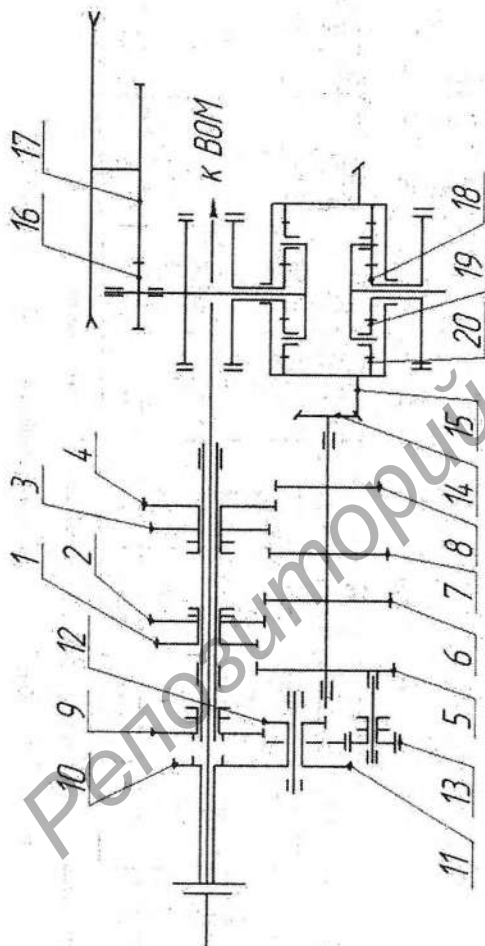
Кинематическая схема силовой передачи трактора Т-70С [32]
